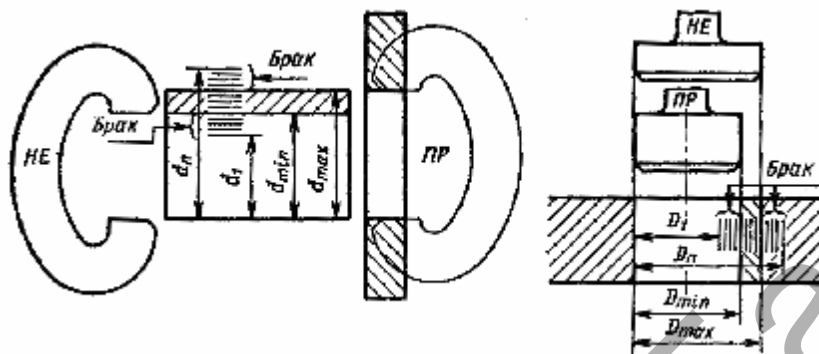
Схема контроля цилиндрических поверхностей гладкими калибрами
